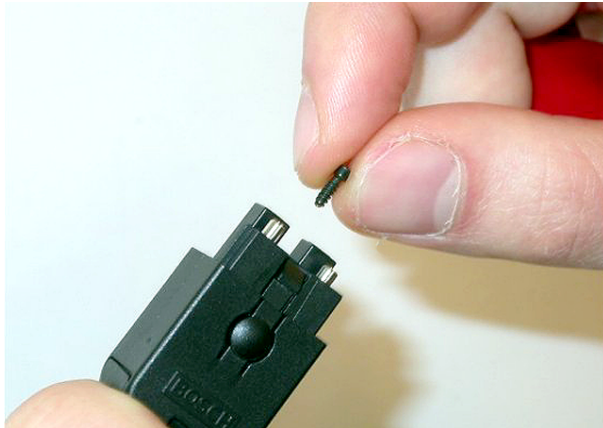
Samenstelling montageblok/achterbehuizing
